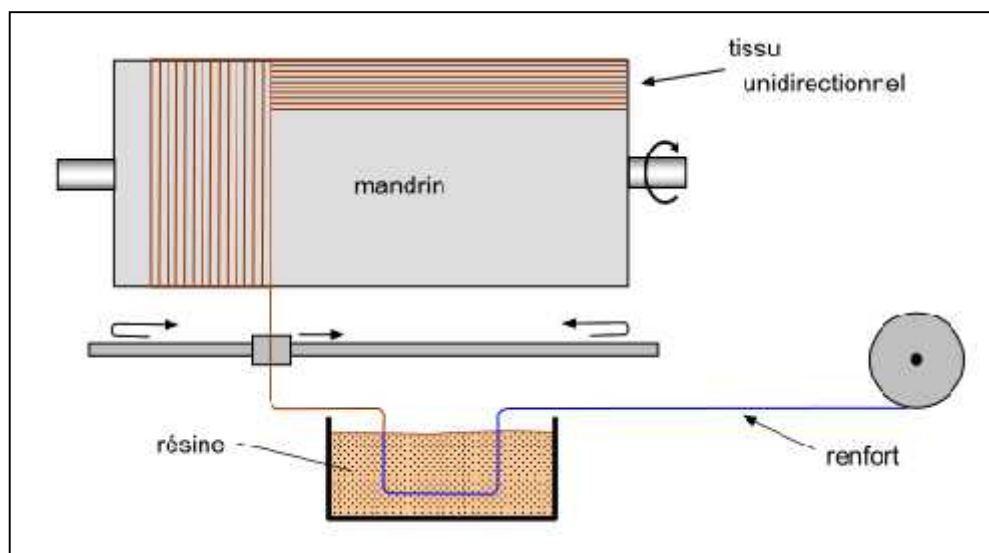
Principe d'enroulement circonférentiel. [6]
